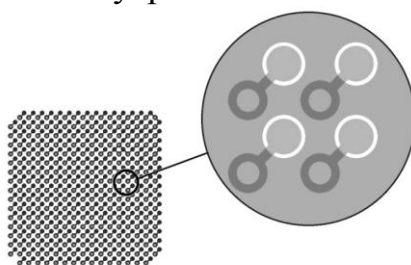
Участок многослойной печатной платы для размещения микросхемы BGA с переходными отверстиями (вид сверху)
